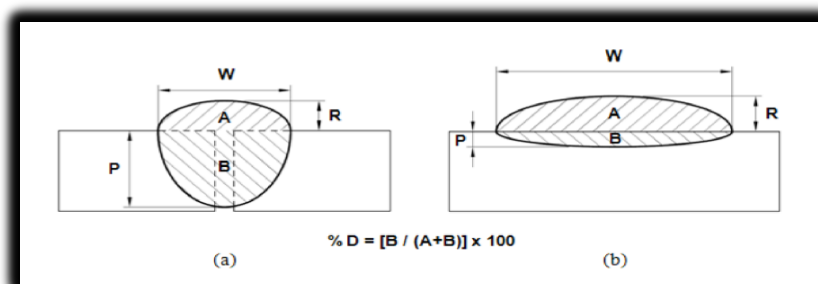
Perfil geométrico desejado do cordão de solda: a) união da junta soldada(aplicações convencionais); b) soldagem de revestimento (Elias, 2013).
